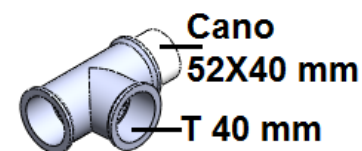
Montagem dos módulos – Módulo 6 – Passo 1
